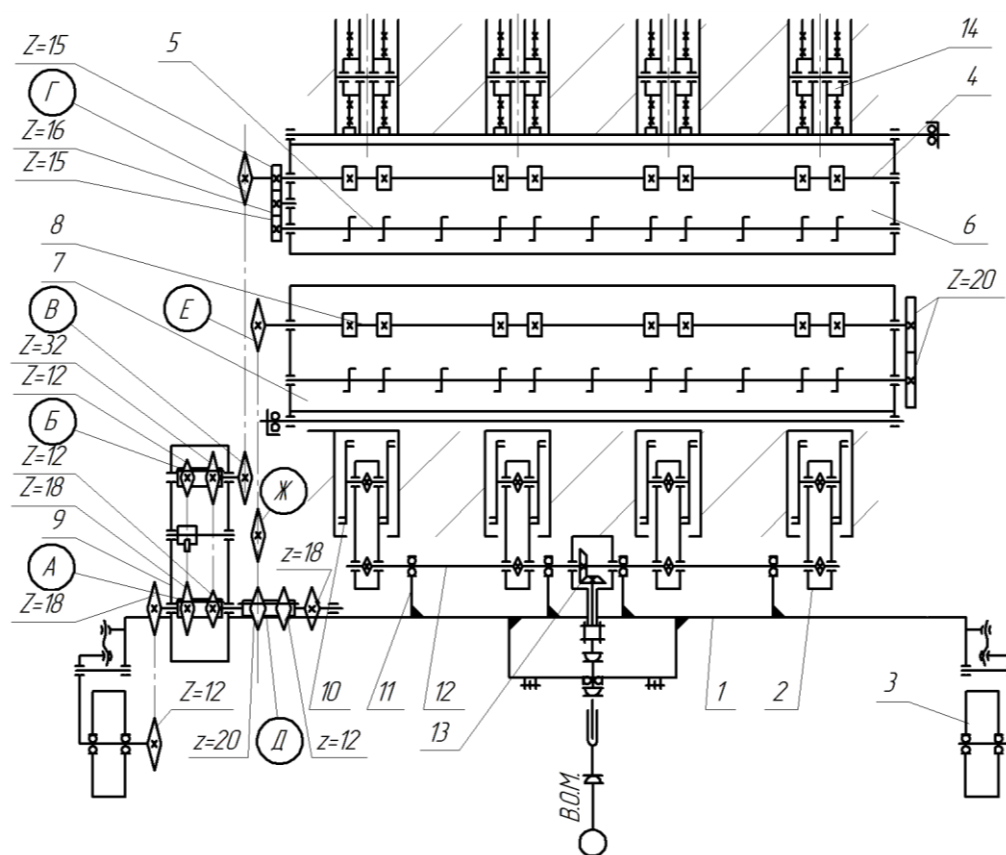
Схема кинематической сеялки полосного посева СДК-2,8М: 1 – рама; 2 – секция привода; 3 – колесо опорно-приводное; 4, 8 – валы семя- и туковывсевающих аппаратов; 5 – ворошилка; 6, 7 – бункеры для семян и туков; 9 – коробка передач; 10 – бороздовскрыватель фрезерный; 11 – опора вала; 12 – вал трансмиссионный; 13 – редуктор центральный; 14 – каток прикатывающий /
